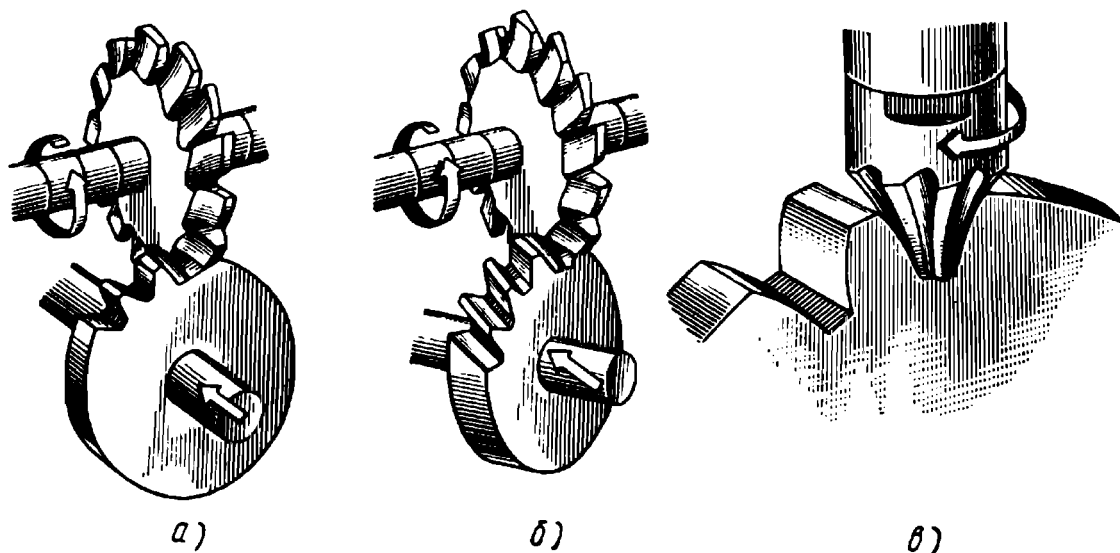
Схемы нарезания зубчатых колес методом копирования: *а* — дисковой модульной фрезой цилиндрического колеса с прямыми зубьями, *б* — дисковой модульной фрезой цилиндрического колеса с винтовыми зубьями, *в* — пальцевой модульной фрезой цилиндрического колеса с прямыми зубьями
